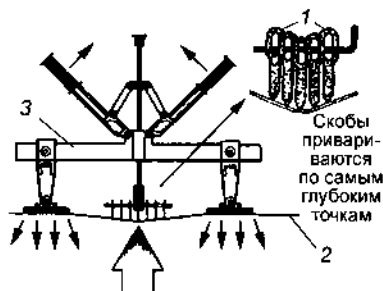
Устранение небольших вмятин вручную: *1* — скобы, прикрепляемые контактной сваркой; *2* — поверхность автомобиля; *3* — приспособление
